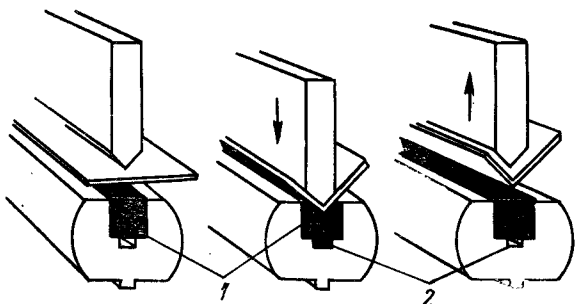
Прямоугольный блок из полиуретана для гибочного штампа:
